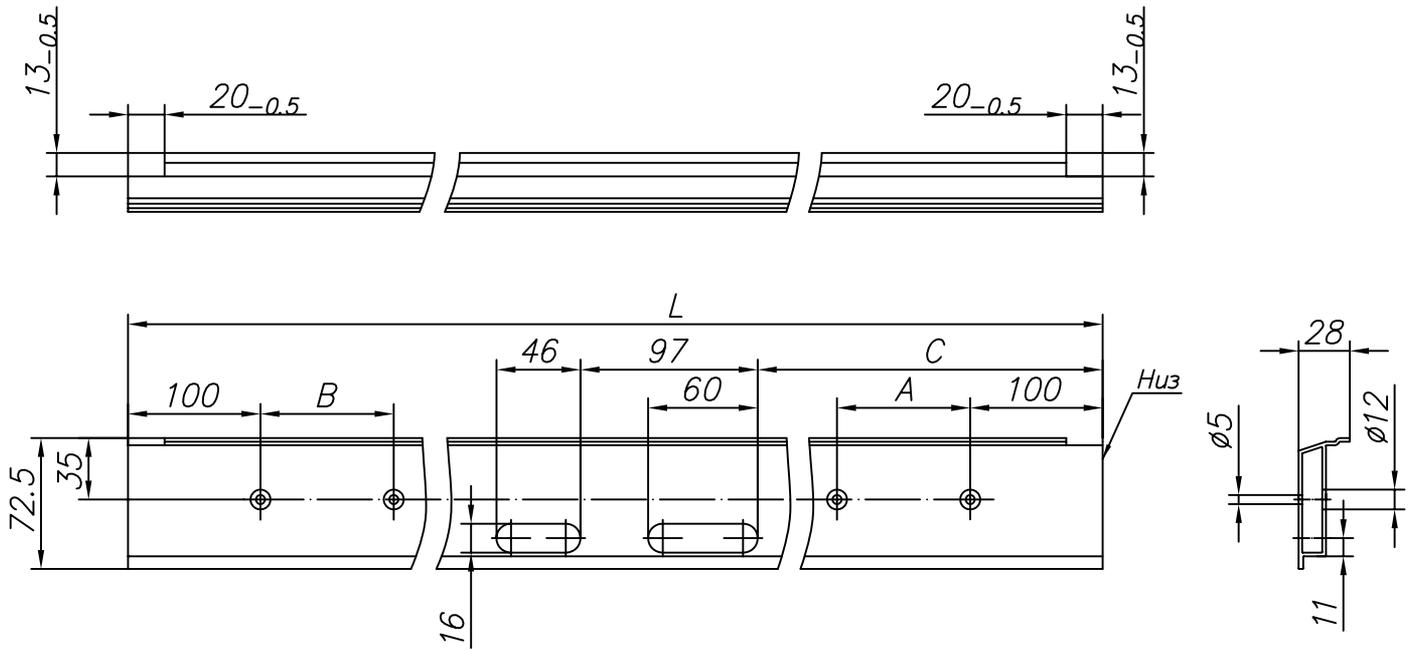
Изготовление притвора с пазом для ответной пластины замка из профиля FLGU.400.0505 (открывание внутрь, вправо)
